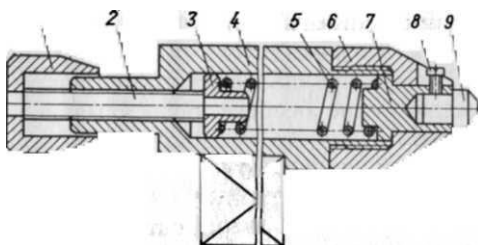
Вигладжувач для обробки зовнішніх циліндричних поверхонь
